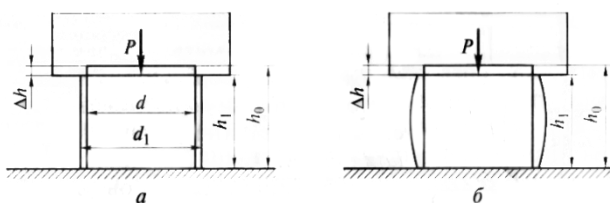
схема осадки цилиндрического образца без трения на торцах (идеальный вариант - *а*), и при наличии трения на торцах (реальный вариант - *б*): h_0 и h_1 — исходный и конечные размеры обрабатываемого изделия, d — диаметр заготовки, d_1 — диаметр детали, Δh — величина осадка, P — усилие осадка.
